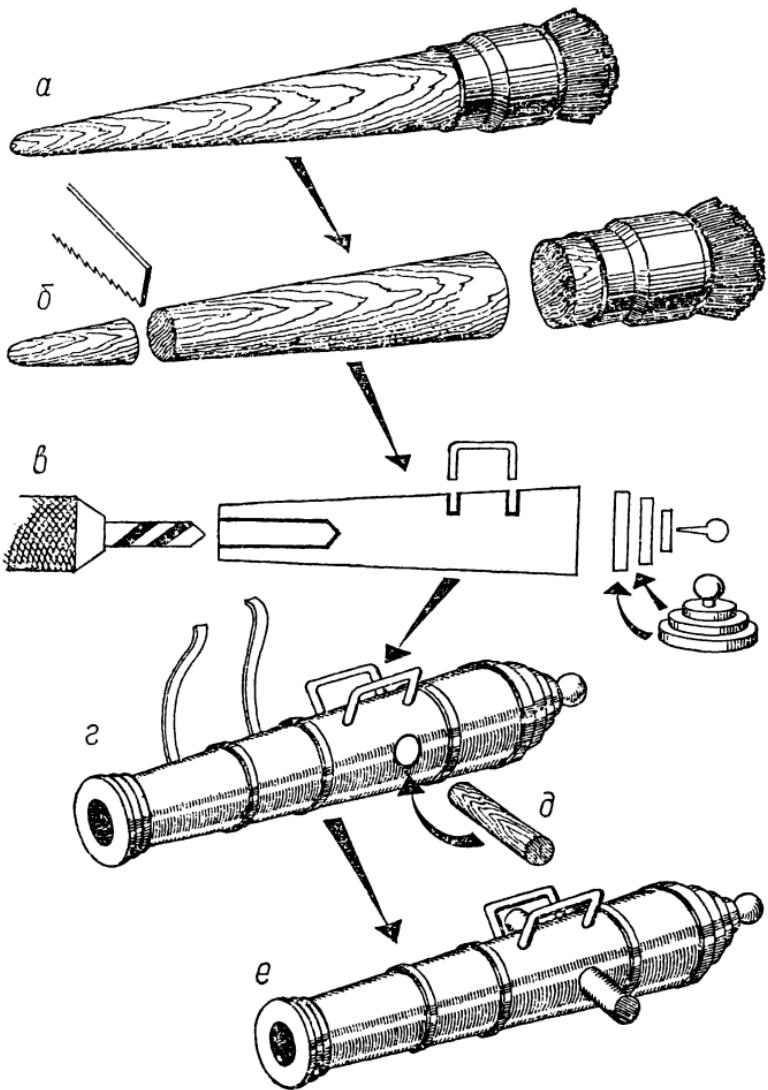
Изготовление ствола модели старинного орудия из дерева:
